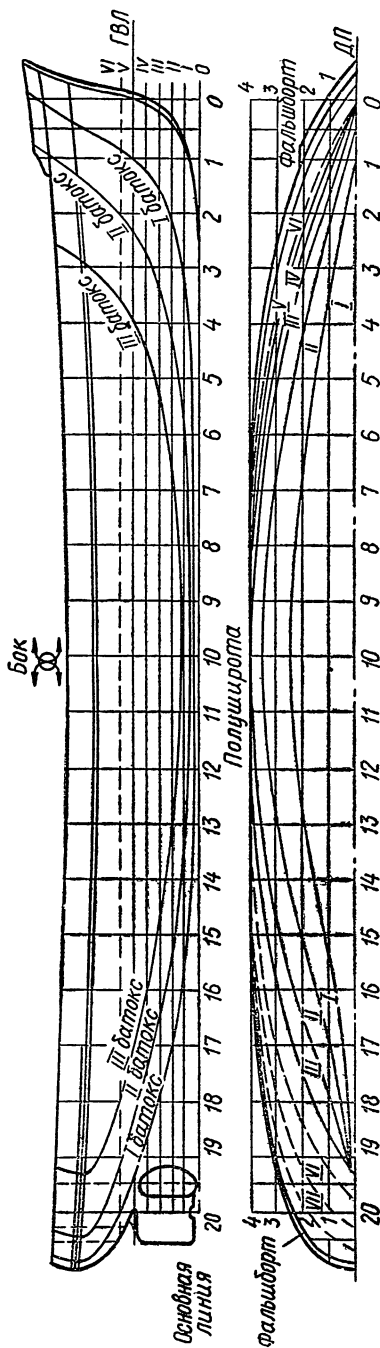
Теоретический чертеж судна (бок и полуширота)
